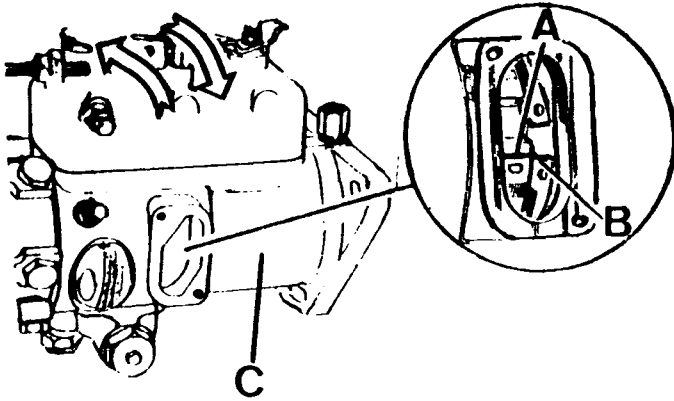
A Ajuste de la bomba una vez -- montada en el motor
